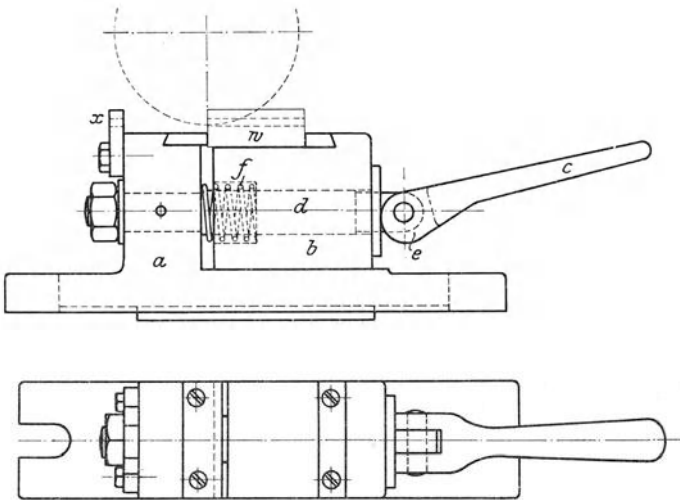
und 164. Durch Hebeldruck spannende Fräsvorrichtung.
